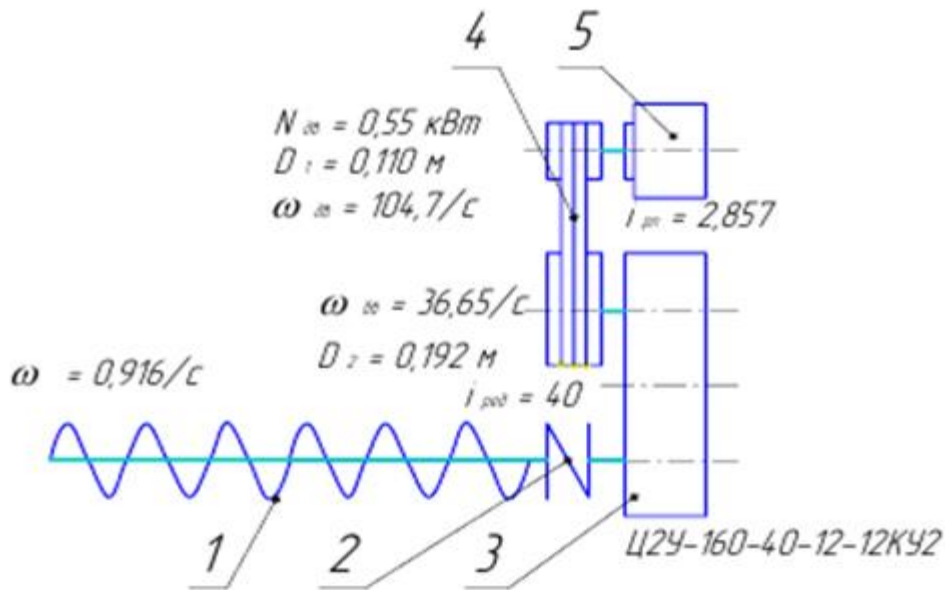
Кінематична схема шнекового пристосування: 1 – шнек; 2 – муфта; 3 – редуктор; 4 – пасова передача; 5 – електродвигун.
